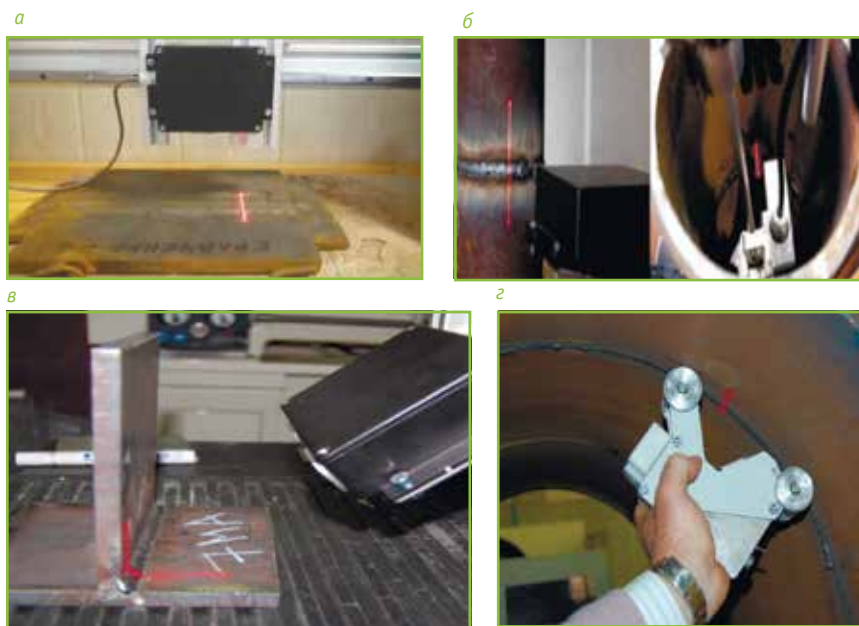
Лазерные сканеры для оценки квалификации сварщиков: а- для оценки КСС стыковых пластин; б- для оценки КСС труб; в- для оценки КСС угло-вых швов пластин; г- ручной мобильный сканер.
